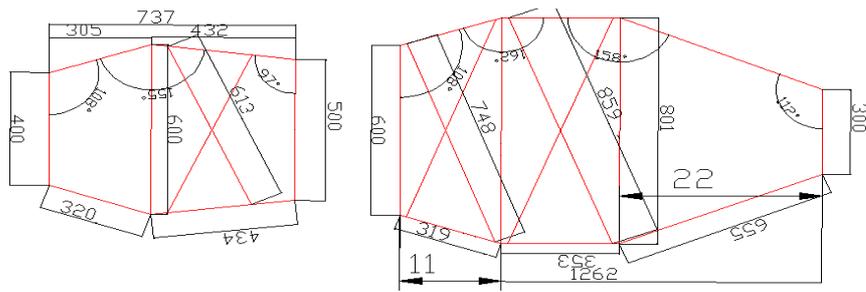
Planos del arco principal y secundario⁸⁶
